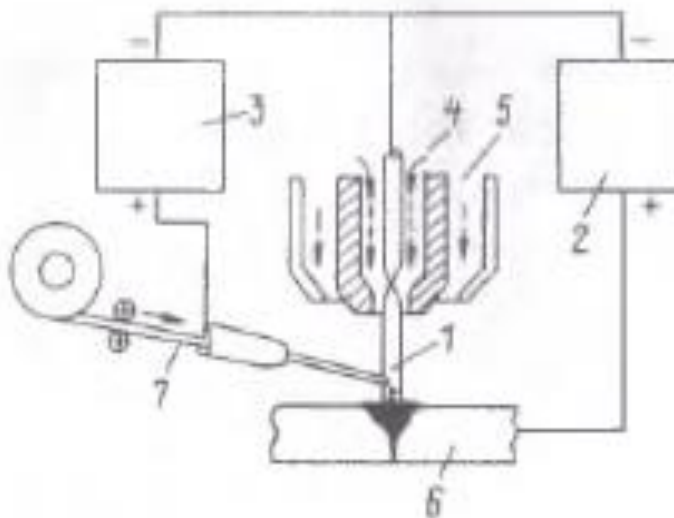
Схема процесса сварки двойной плазменной дугой с токоведущей присадочной проволокой: 1- плазменная дуга; 2- источник питания дуги «электрод-изделие»; 3- источник питания присадочной проволоки; 4- плазмообразующий газ; 5-защитный газ; 6- изделие; 7 сварочная проволока
